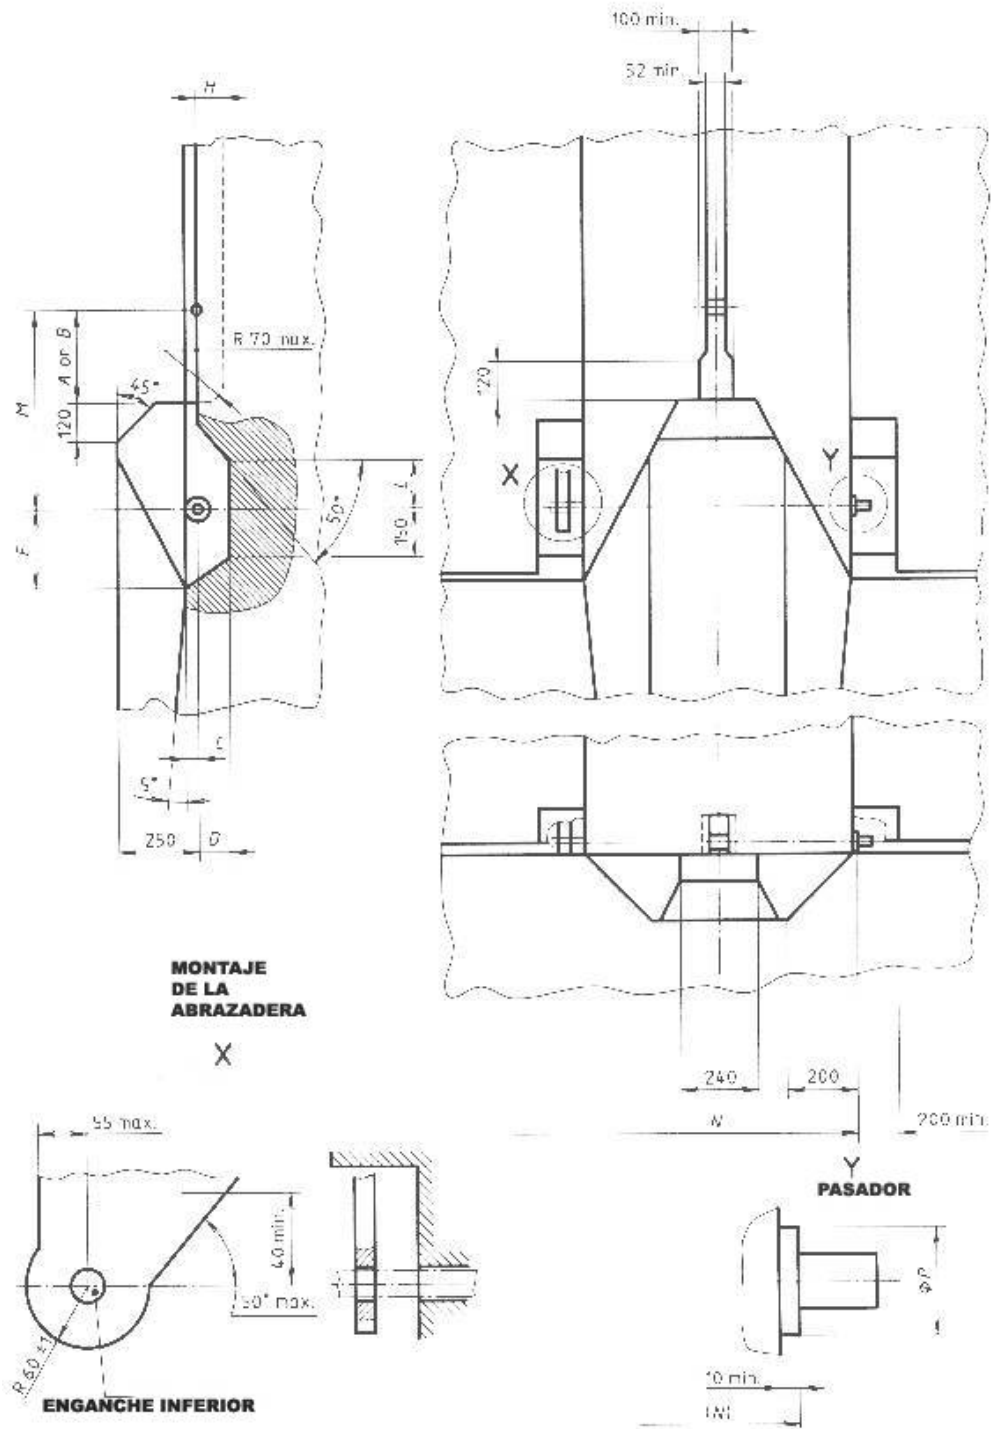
Zona de despeje de los implementos donde el acceso al paso de rosca no se extenderá hacia adelante en posición elevada verticalmente. (vista en detalles)
